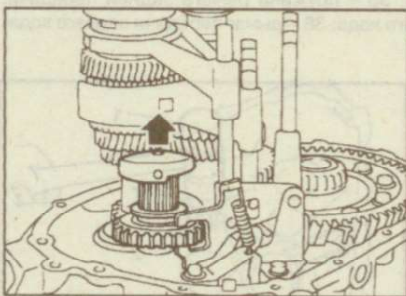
Снятие вала промежуточной шестерни заднего хода и шестерни заднего хода
